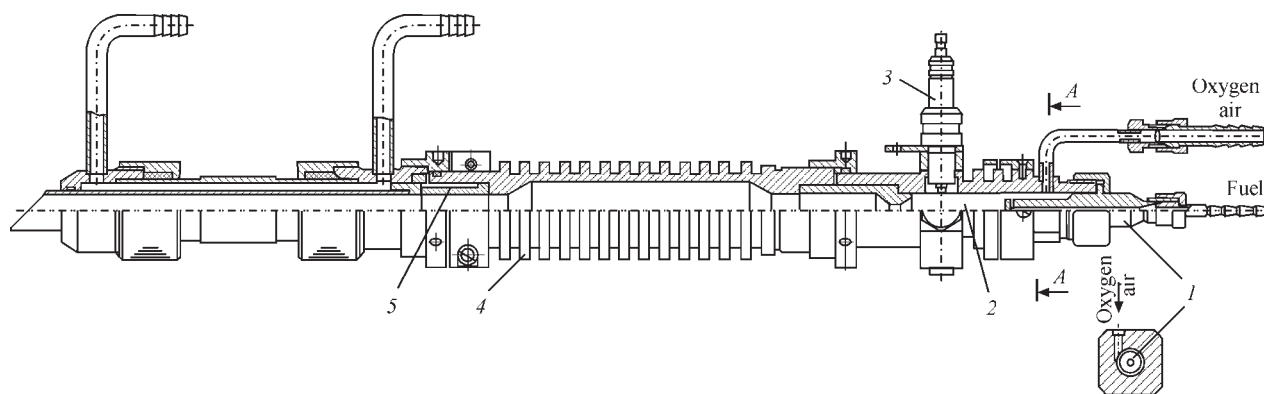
Безклапанний детонаційний пристрій з циліндричною форкамерою
